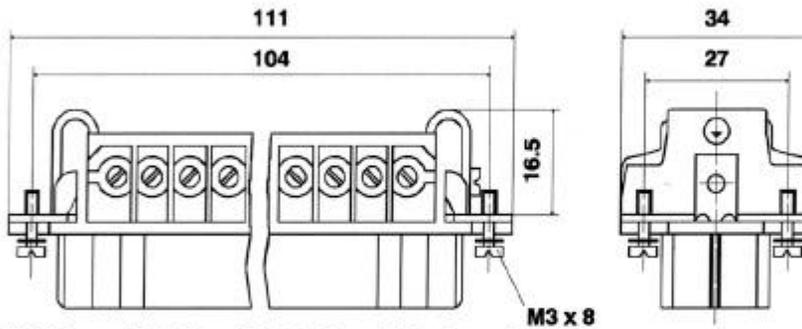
Anschlußstecker mit Buchseneinsatz
